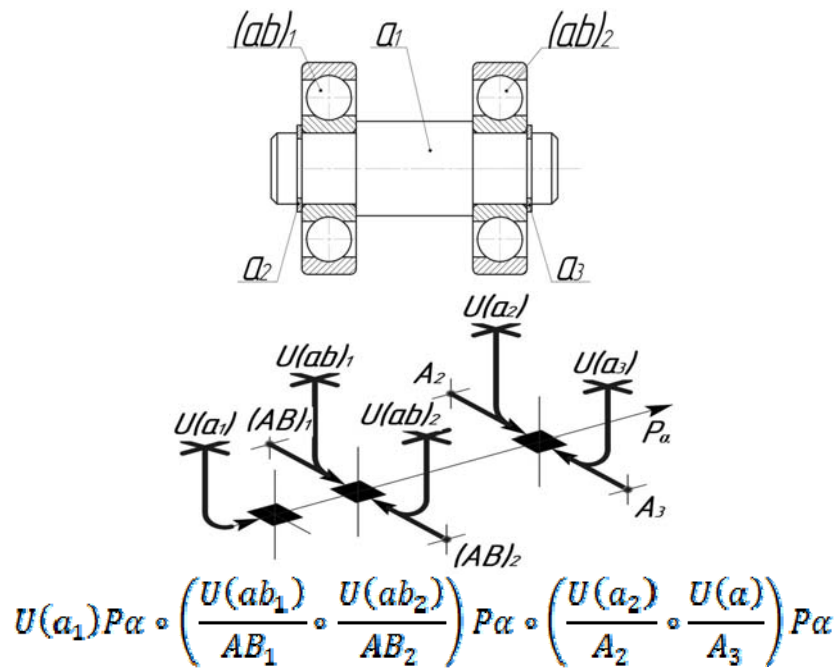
Вал с двумя подшипниками и стопорными кольцами
